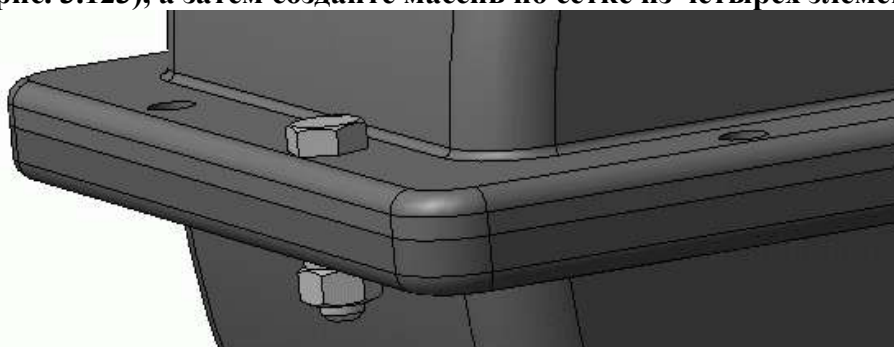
Болтовое соединение фланцев корпуса и крышки
